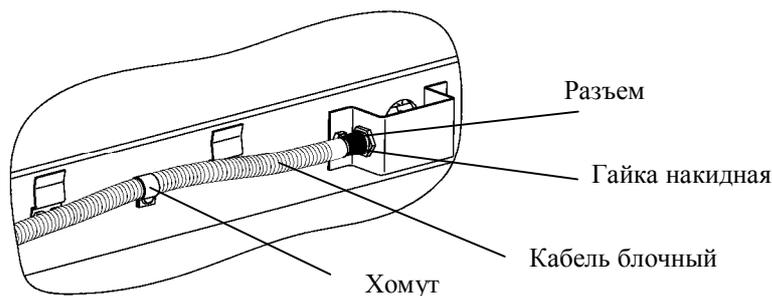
Соединение кабеля блочного с платформой весовой
